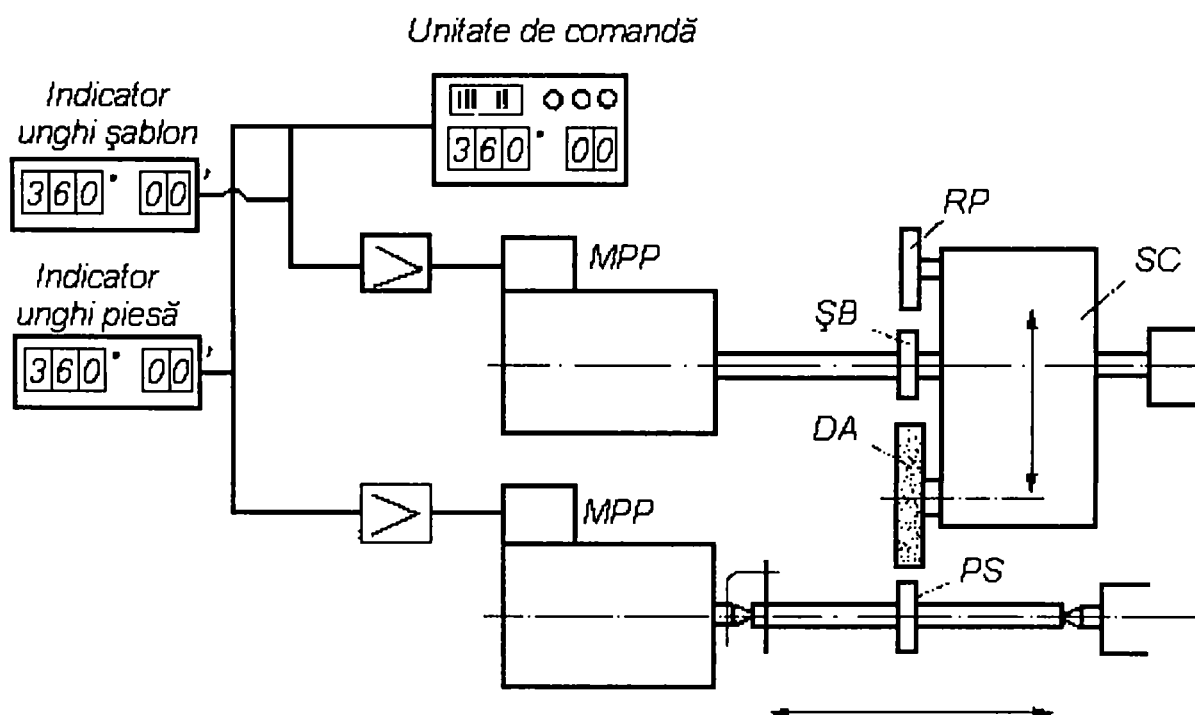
Mașina de rectificat profilul camelor plane cu mișcare de translație
